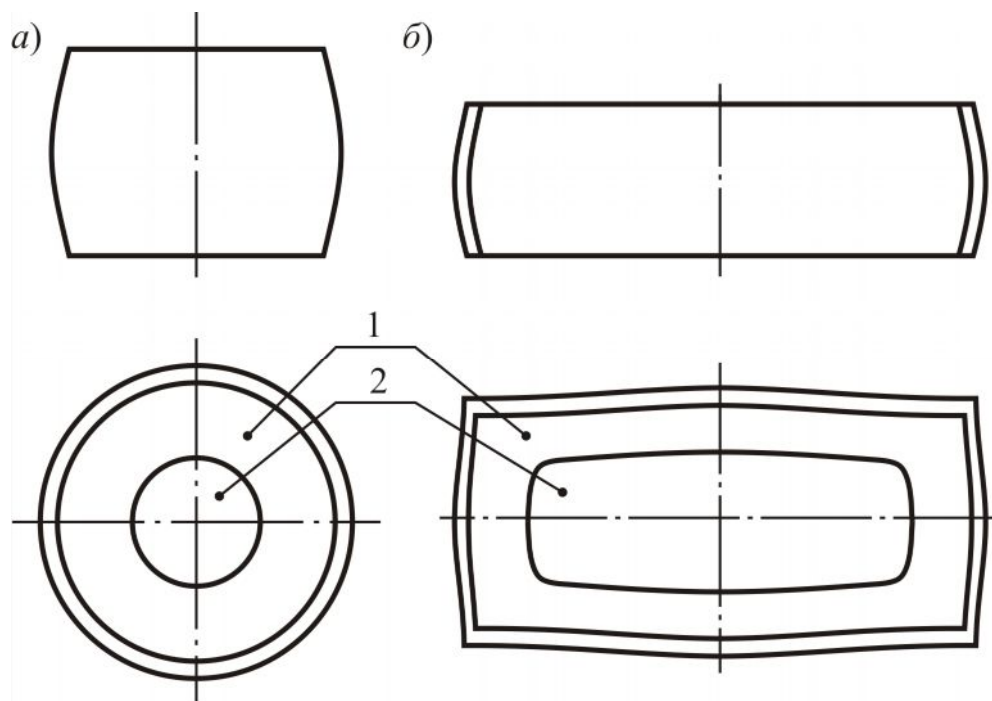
Зоны скольжения (1) и торможения (2) на контактной поверхности цилиндрической (а) и призматической (б) заготовок при свободной осадке плоскопараллельными плитами
